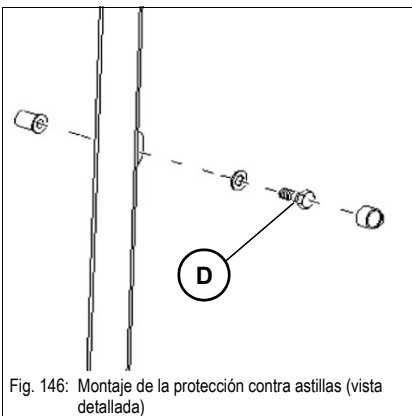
Montaje de la protección contra astillas (vista detallada)
